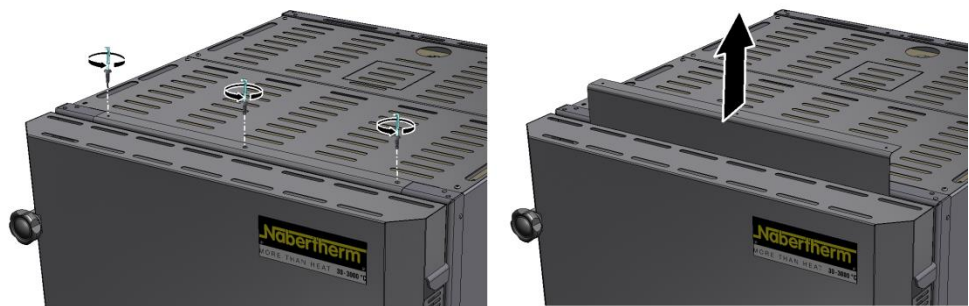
Демонтаж защитной планки бортика (рисунок примерный)
